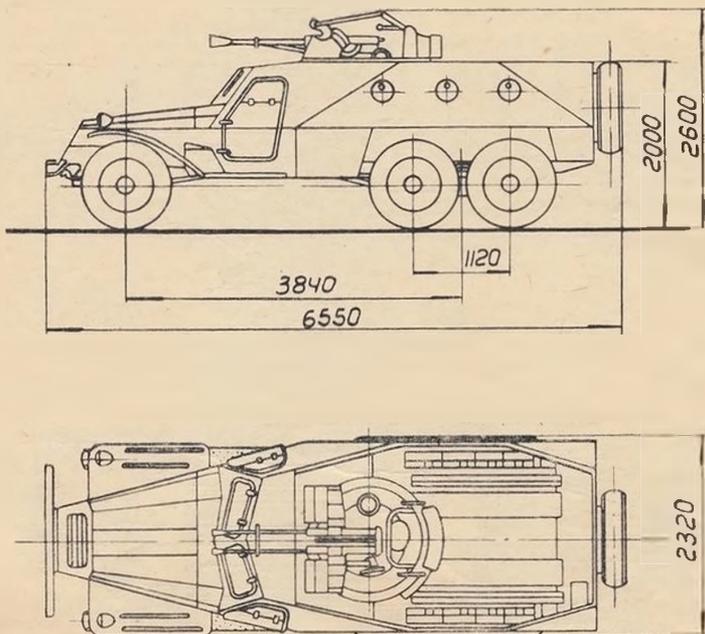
Общий вид и габаритные размеры бронетранспортера БТР-152А.
